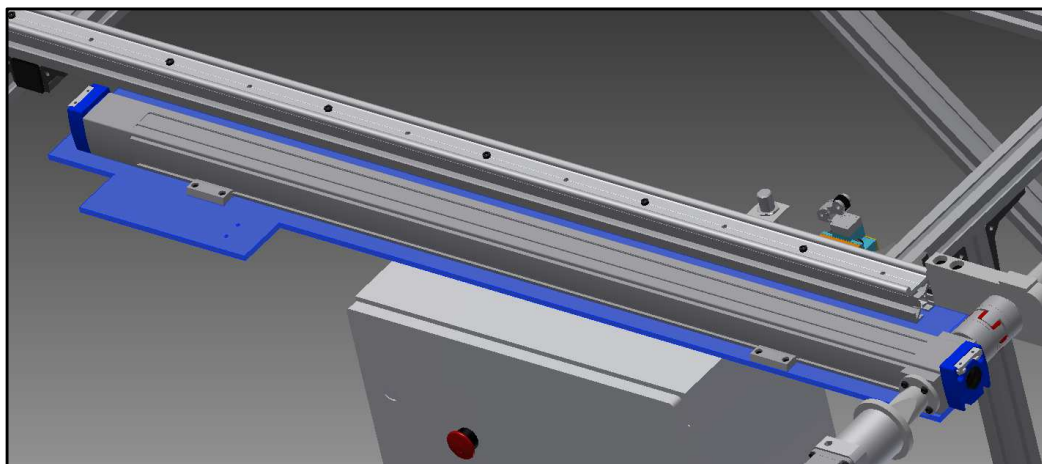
Chapa de apoyo estructural izquierdo en el montaje.
